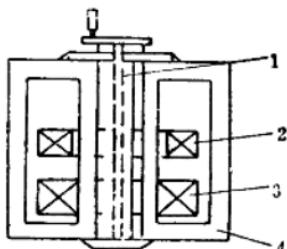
7 动圈式交流弧焊变压器电磁结构原理图
